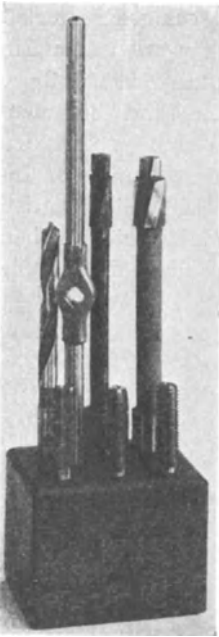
Zusammengehörige Werkzeuge auf einem Holzklötz.
